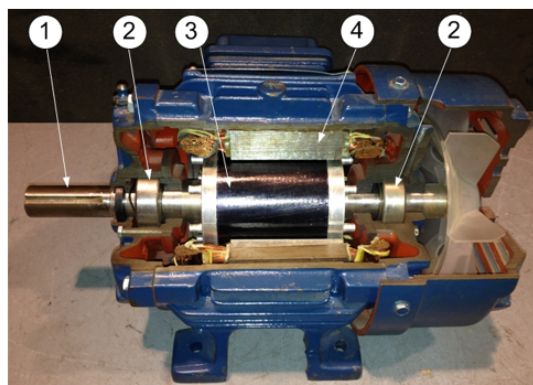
Partes de un motor de inducción: 1. Eje o flecha, 2. Rodamiento, 3. Rotor, 4. Estator
